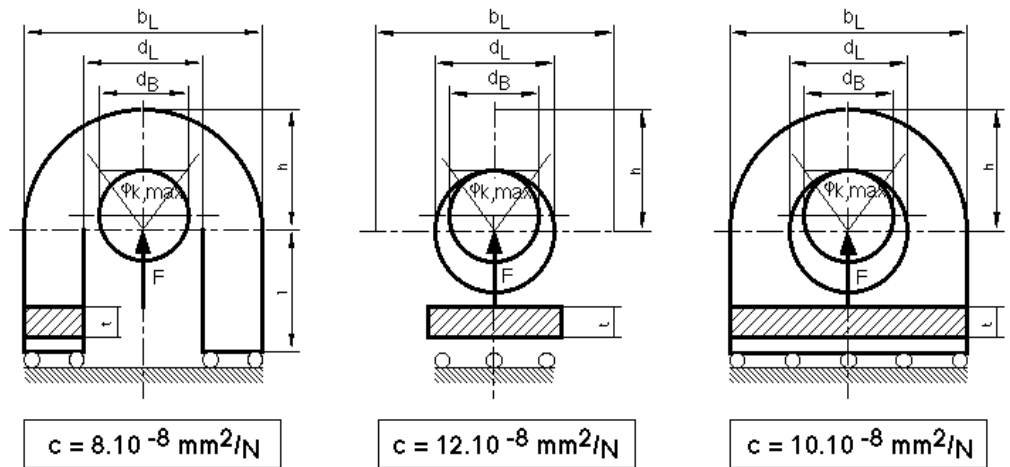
Drei typische Formen von Bolzen-Lasche-Verbindungen mit spielbehafteten Bolzen und ihre Steifigkeiten. Links: Lasche. Mittig: Augenring. Rechts: Augenstab
